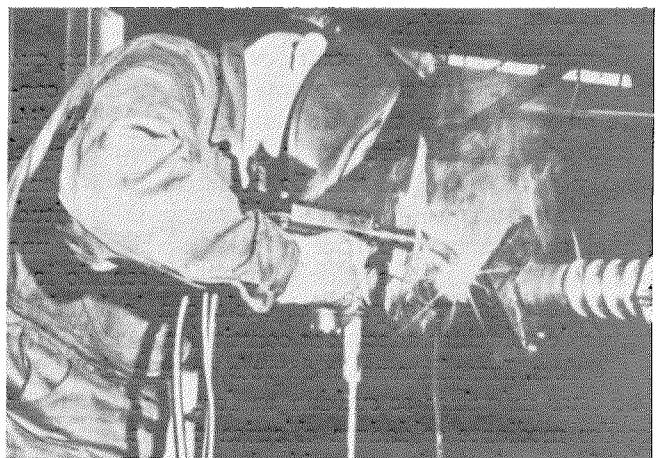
Soldadura de aluminio por el procedimiento MIG.
